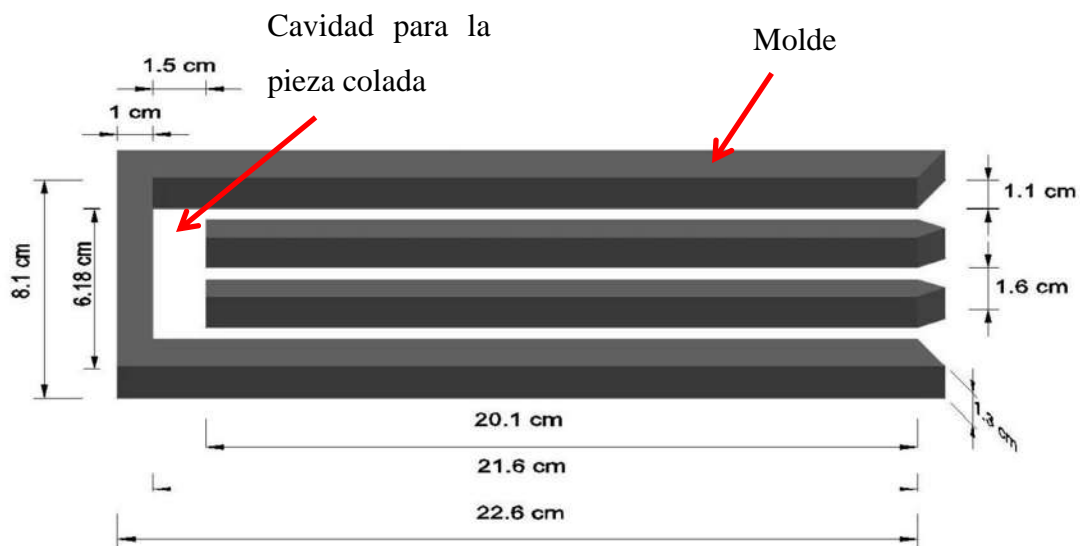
4: Dimensiones del molde donde se coló el material compuesto Al-6061/TiC.
